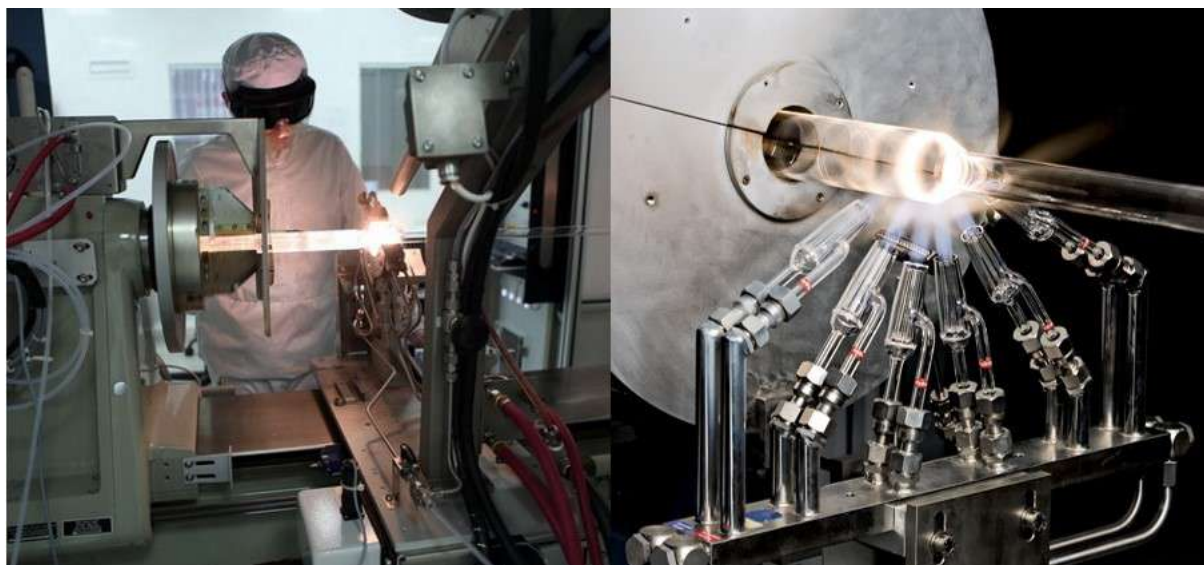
Внешний вид тепломеханического станка для MCVD
